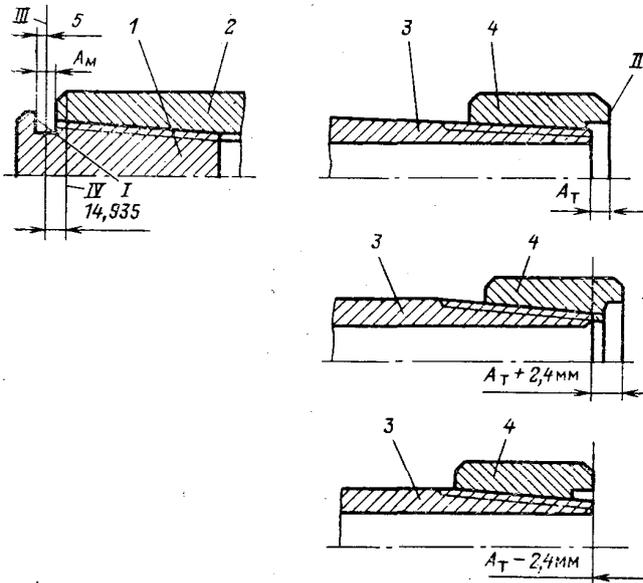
Схема проверки резьбы буровых труб и муфт к ним по ГОСТ 631—75 резьбовыми калибрами:
